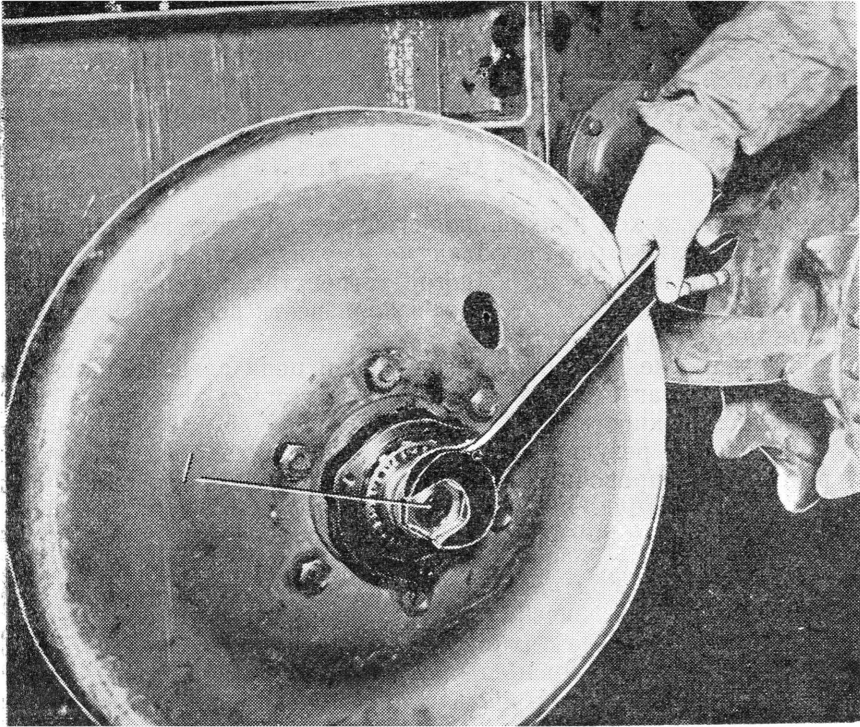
Регулировка зазоров в конических подшипниках опорных катков:
